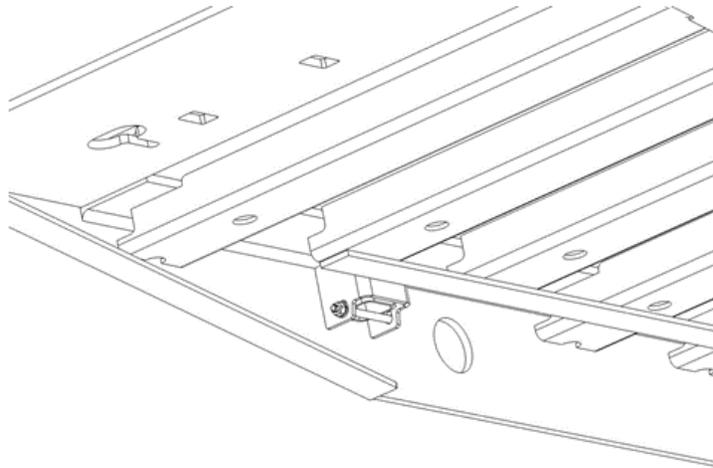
BOULONS RETENANT LES RAILS À 1 PO AU-DESSUS DU PLANCHER (VUE À PARTIR DE SOUS LE PLANCHER)
